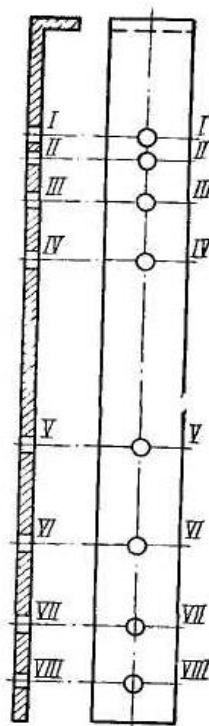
Планка-шаблон для измерения втулки цилиндра
